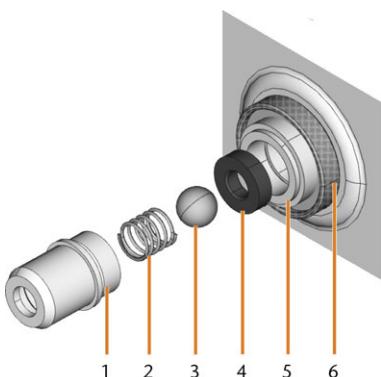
COMPONENTES DEL ENGANCHE DEL DEPÓSITO DE LÍQUIDO REFRIGERANTE
